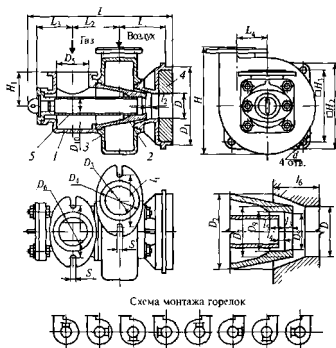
Турбулентные горелки типа ГТН для газов с низкой теплотой сгорания: 1 — газовый корпус; 2 — газовое сопло; 3 — воздушный корпус; 4 — горелочный камень; 5 — гляделка
